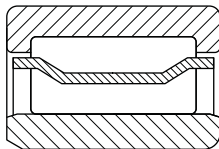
Geteilter, gefräster, innenringgeführter Messingkäfig mit „Fingern“
